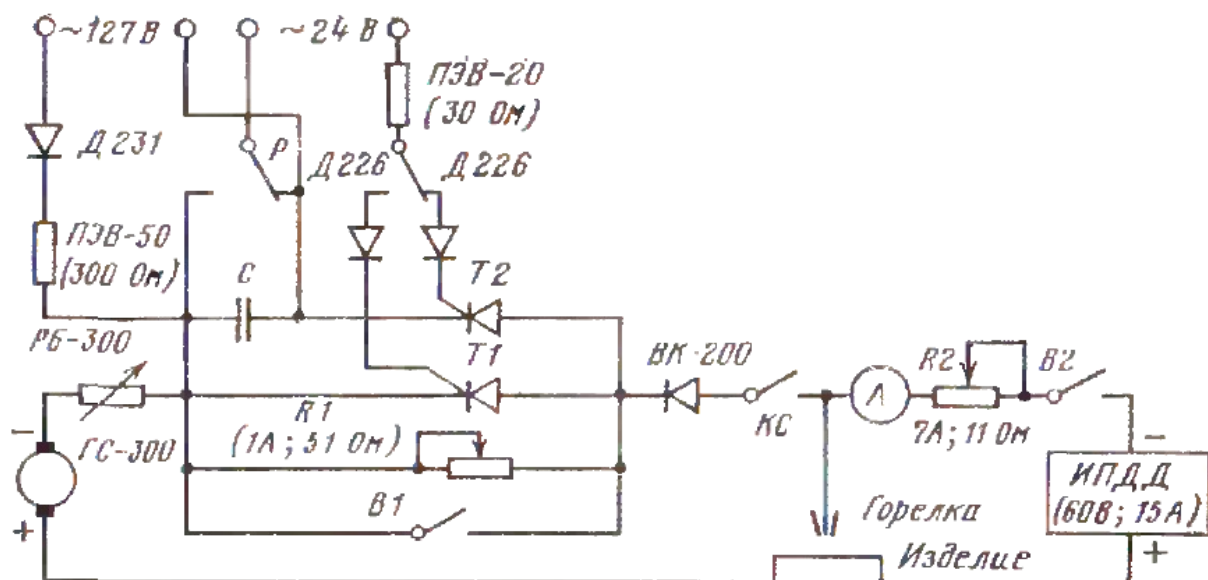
Принципиальная электрическая схема прерывателя. КС – контакты сварочного контактора; В1, В2, Р – переключатели [4]
